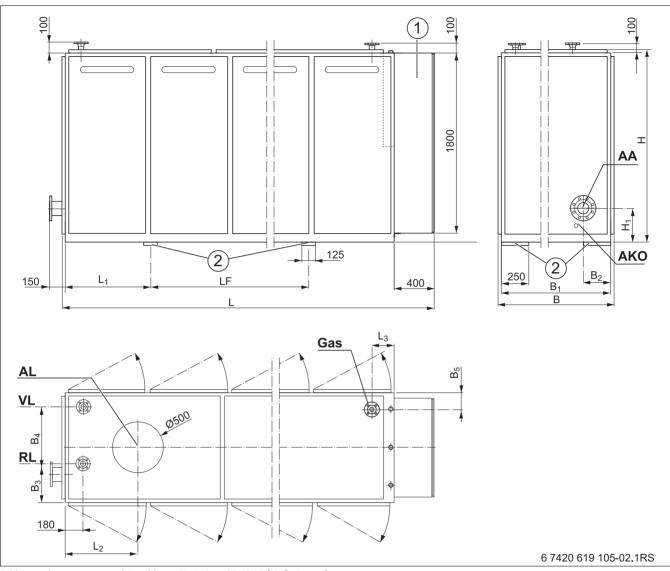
Abmessungen und Anschlüsse EN140 und EN240 (Maße in mm)
